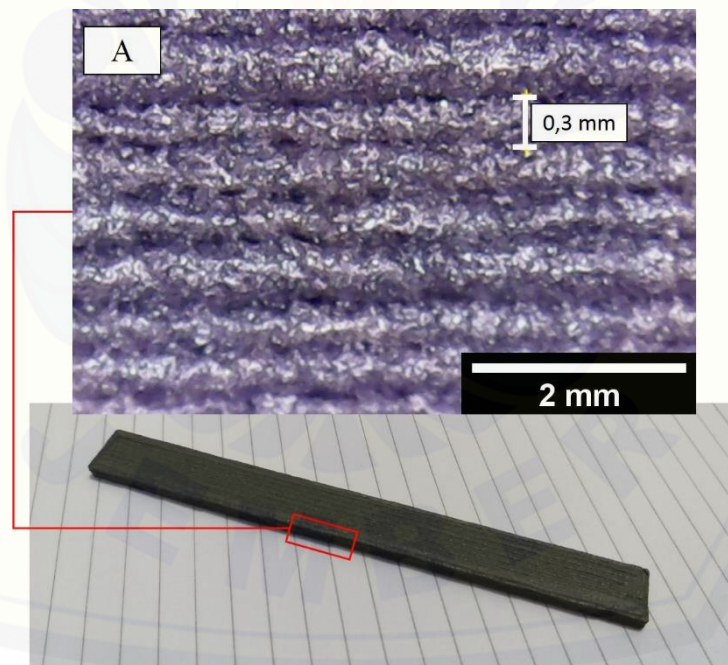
Hasil 3D *printing* spesimen uji *bending
